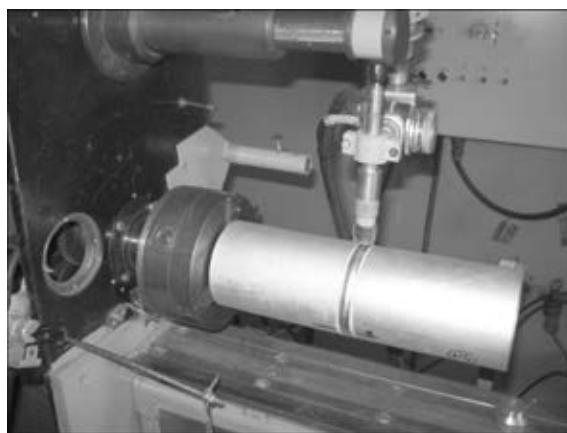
Аргонодуговая сварка образцов кольцевых стыков из сплава АМгб
